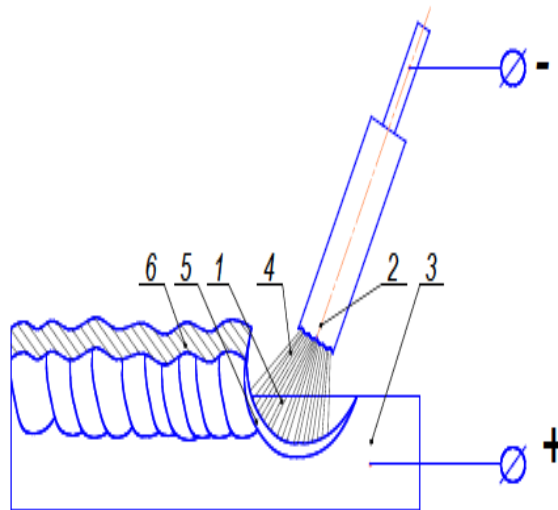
Ручне дугове зварювання покритим електродом: 1 – дуга; 2 – електрод; 3 – метал; 4 – краплі; 5 – зварювальна ванна; 6 – шлакова кірка
